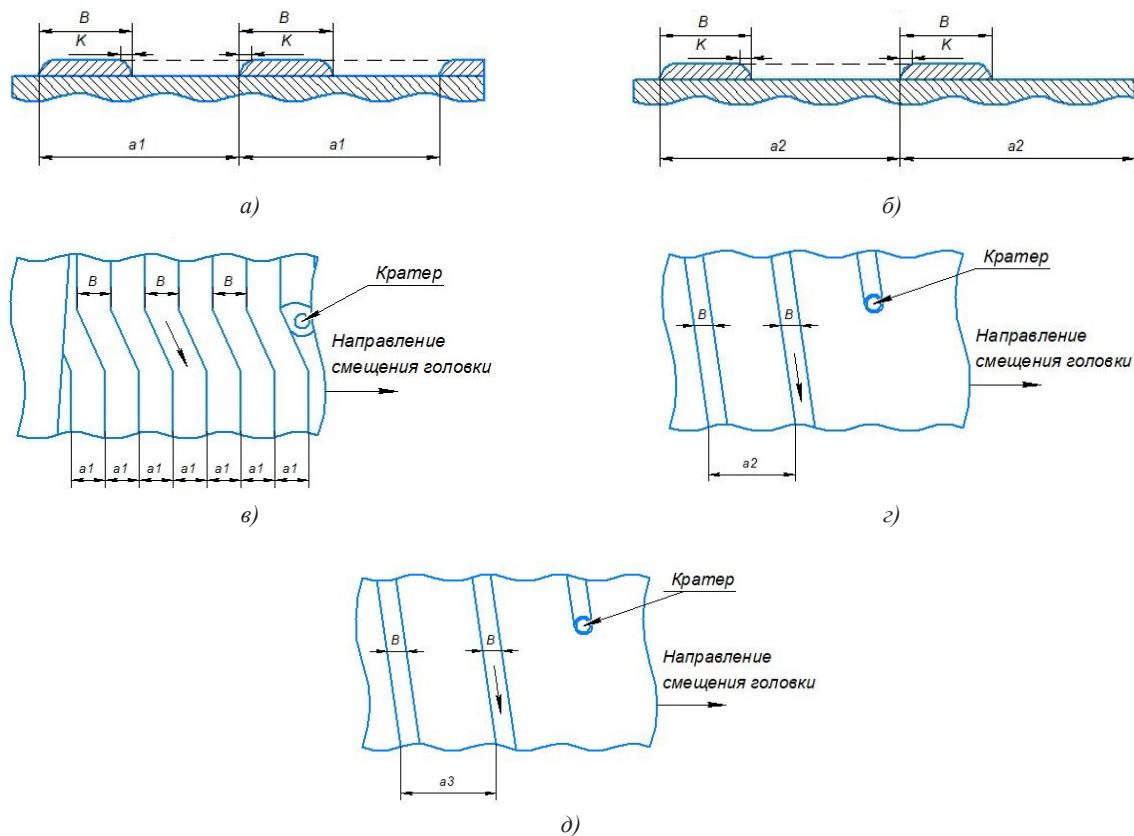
Схема наплавки валиков заданным шагом, а — схема наплавки с двойным шагом ($n=1$); б — схема наплавки с тройным шагом ($n=2$); в — наплавка «слаломом» с одинарным шагом ($n=0$); г — наплавка «раздвинутыми» валиками с двойным шагом ($n=1$); д — наплавка по спирали с тройным шагом ($n=2$)
